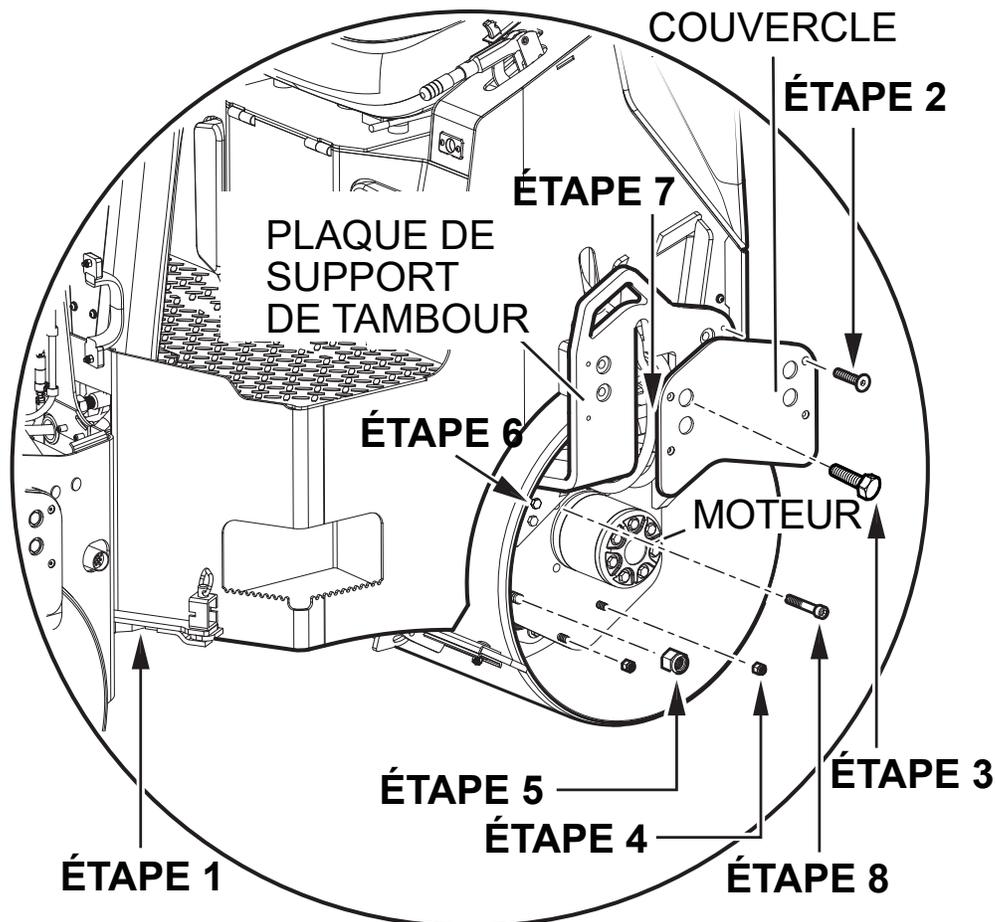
Démontage/Installation du roulement (Tambour arrière - Côté droit)
